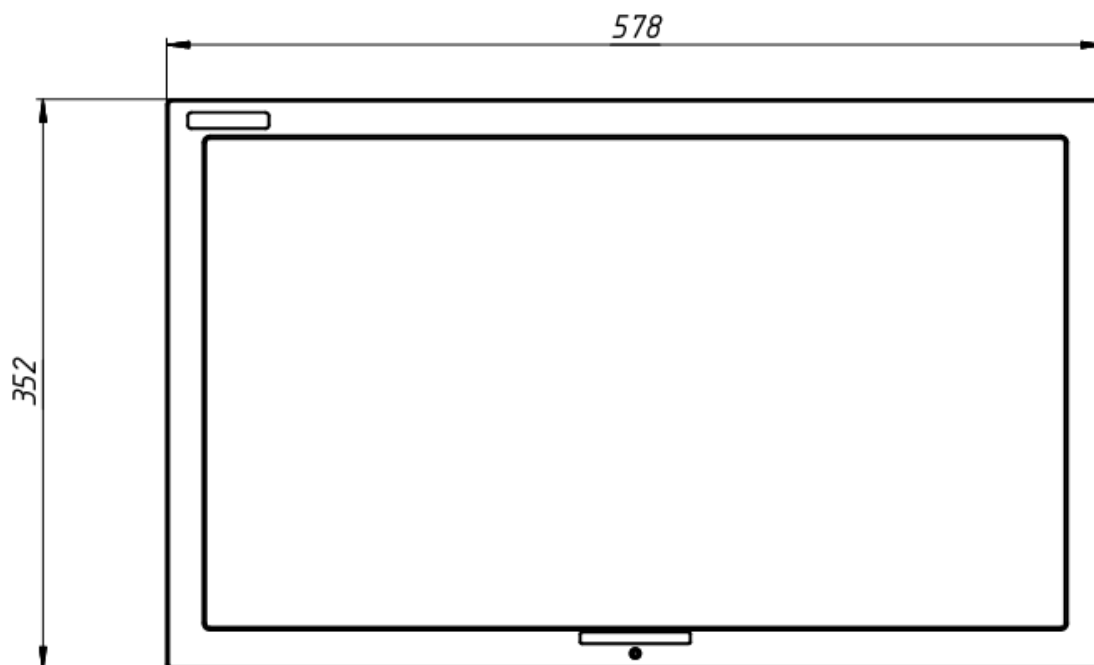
Габаритный чертёж лицевой части ПИ
